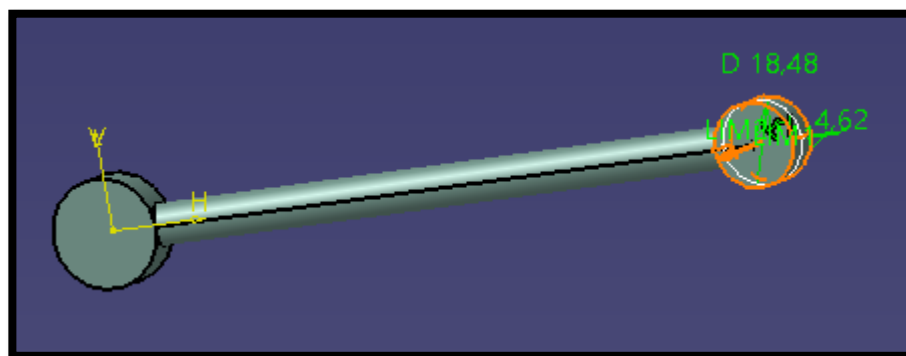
Seat mounting frame 11: Union trim.2 brazo oscilante superior
